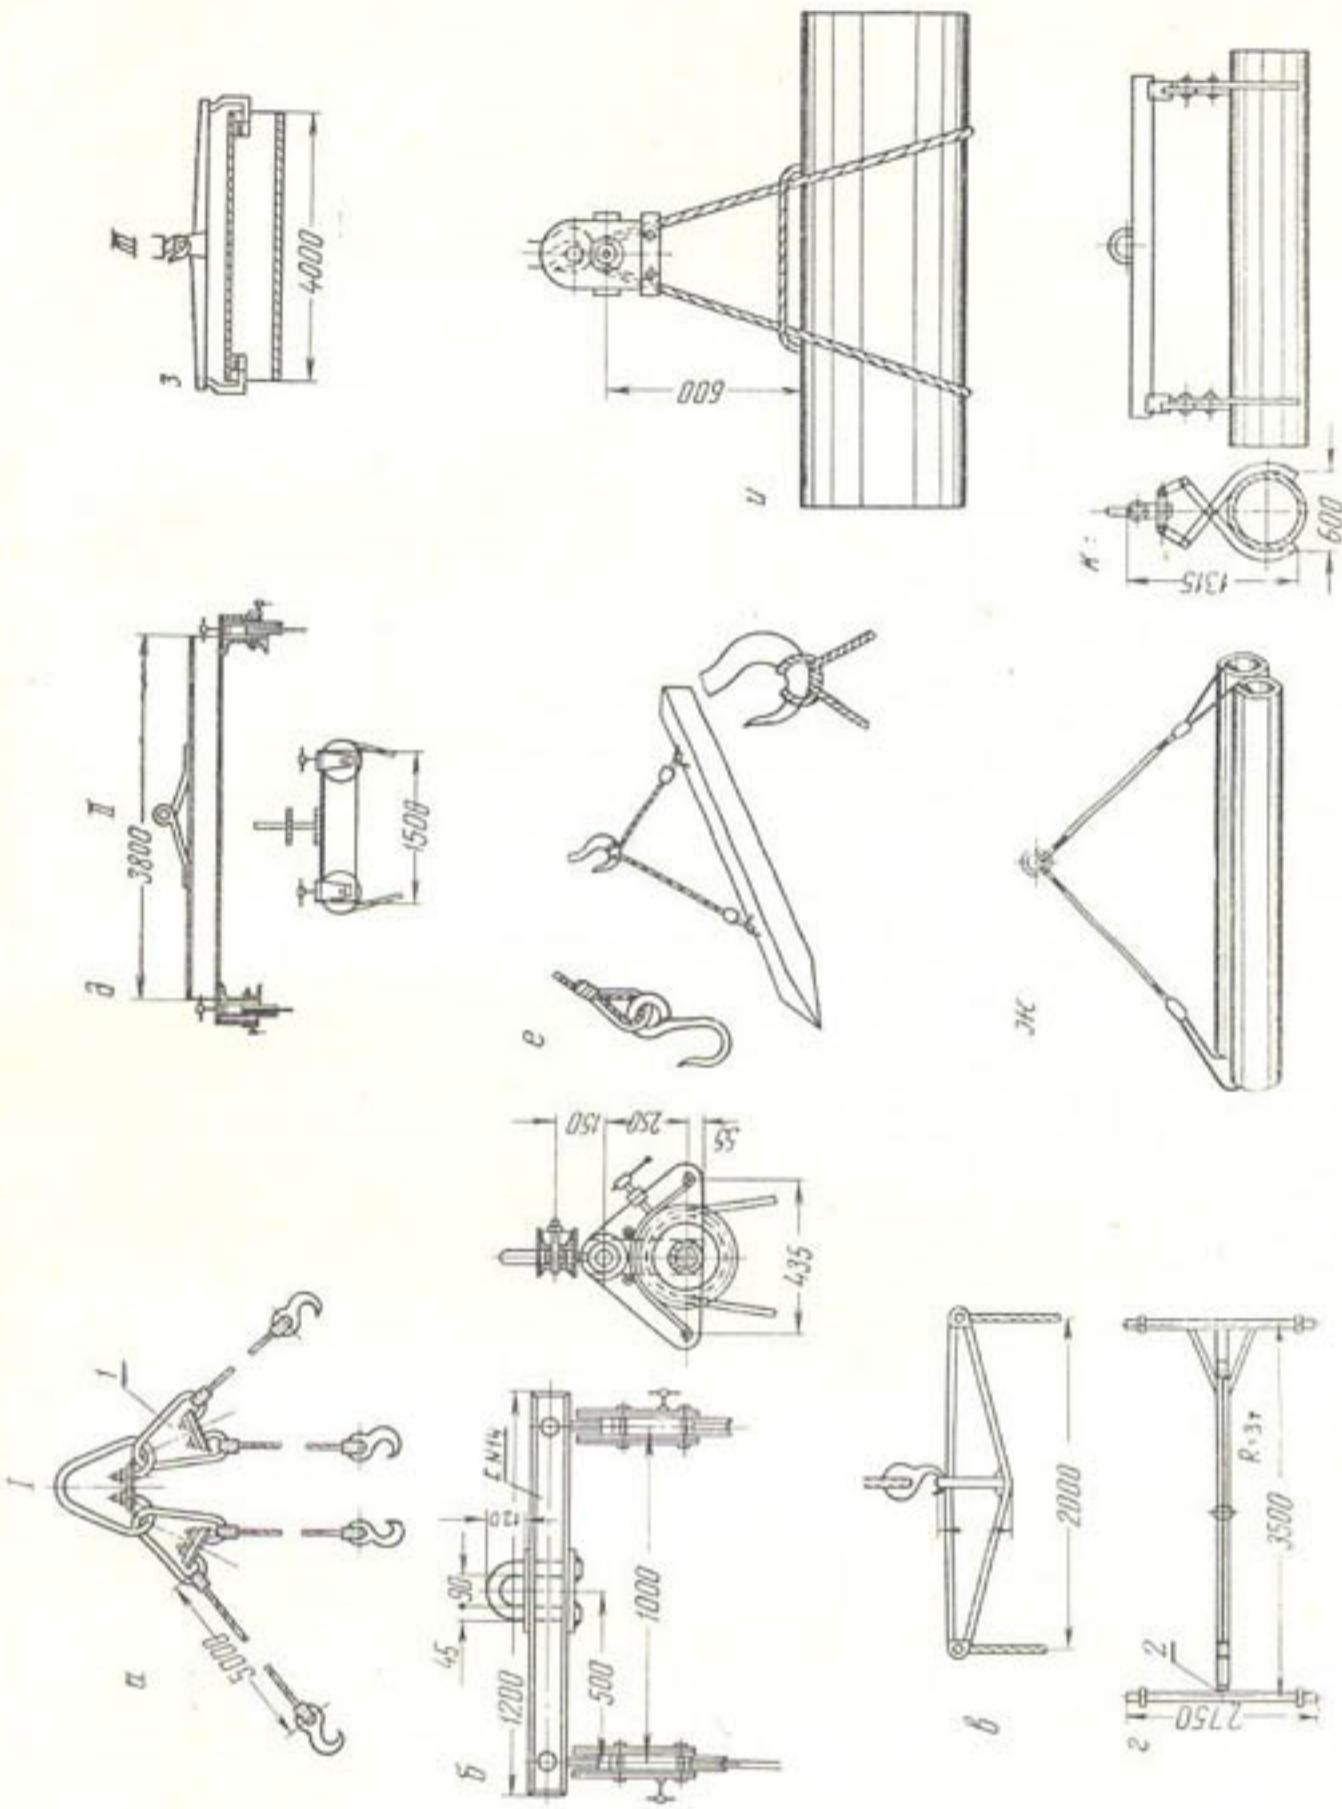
Захватные приспособления для погрузочно-разгрузочных операций:
